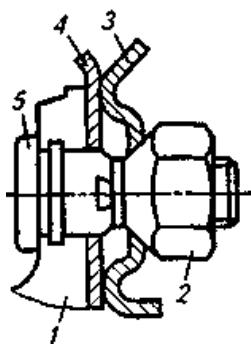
Крепление колеса легкового автомобиля: 1 — ступица; 2 — гайка; 3 — диск колеса; 4 — тормозной барабан; 5 — болт
